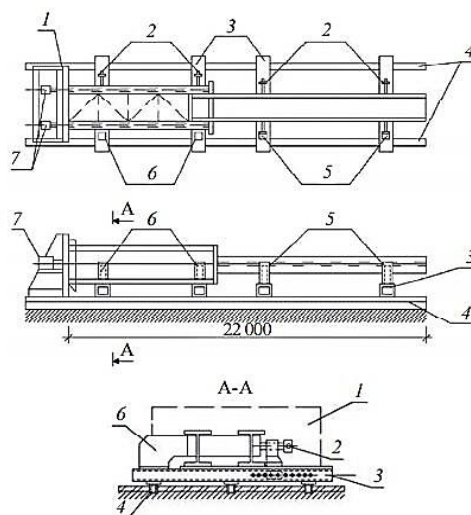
Кондуктор для складання решітчастих колон: 1 - торцевий упор; 2 - гвинтовий упор; 3 - опорні балки; 4 - закладні опори; 5, 6 - боковий упор; 7 – пневмопритискач
